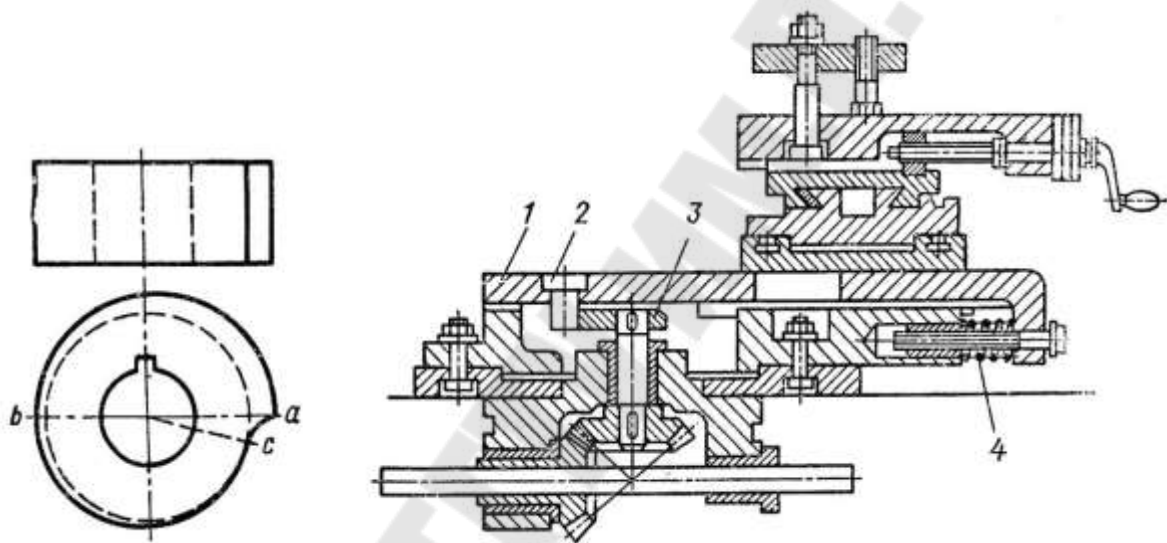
Эскиз сменного кулачка и суппорта токарно-затыловочного станка
